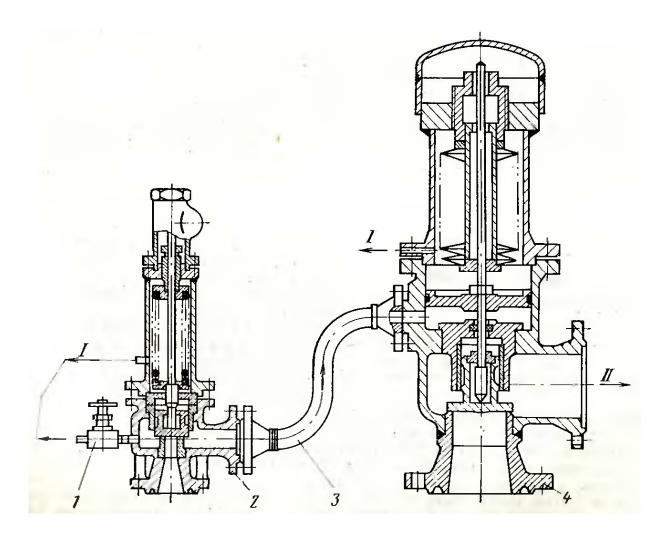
Предохранительный клапан со вспомогательным устройством I- сброс в линию атмосферного давления; II- сброс в линию низкого давления; 1- игольчатый вентиль, 2 - импульсный клапан; 3 - соединительная труба; 4 - предохранительный клапан
